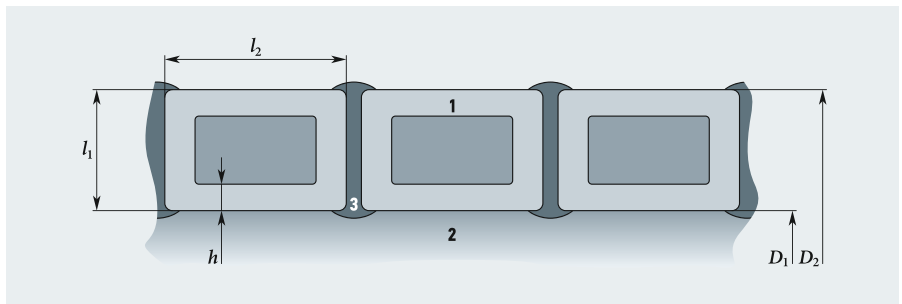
(1 — профиль; 2 — отверстие в профиле; 3 — сварной шов)
